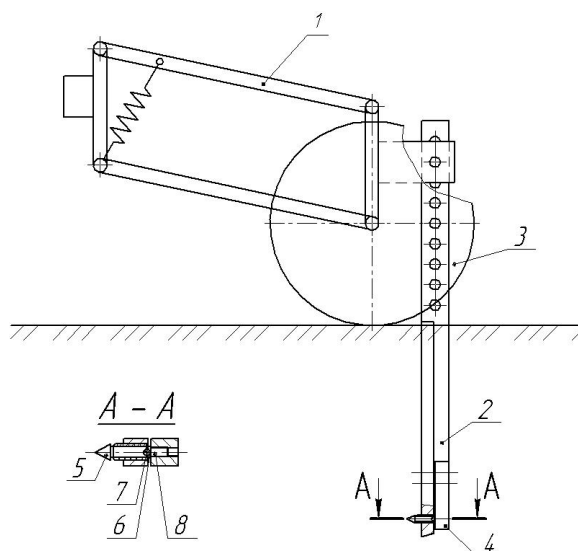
Конструкция прибора для непрерывного измерения твердости почвы.
